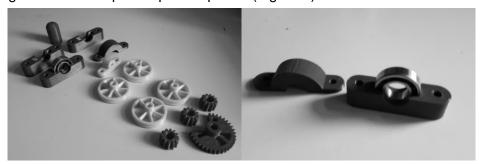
Piezas de la máquina realizadas en impresión 3D.
